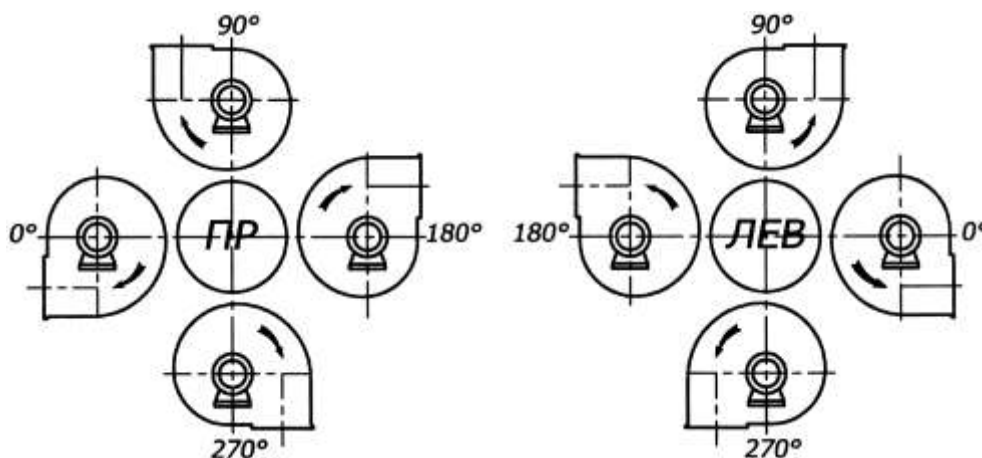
Схема углов разворота корпуса тягодутьевой машины.
